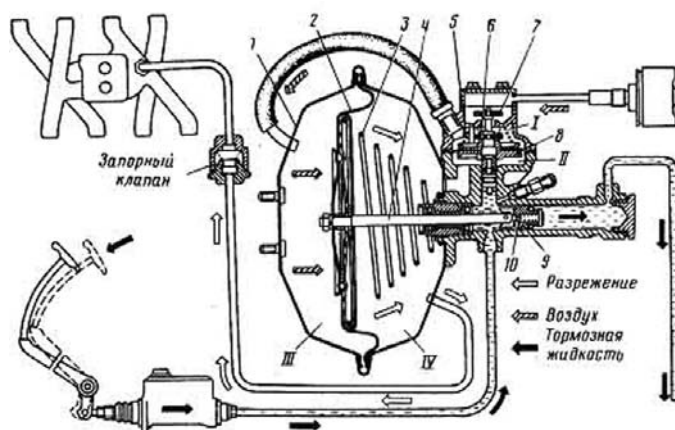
Схема гидровакуумного усилителя автомобиля ГАЗ-53-12 (момент торможения): I, II, III, IV — полости; 7 — корпус; 2 — диафрагма; 3 — пружина; 4 — шток; 5 — пружина; 6 — вакуумный клапан; 7 — атмосферный клапан; 8 — поршень клапана управления; 9 — манжета поршня; 10 — клапан поршня
